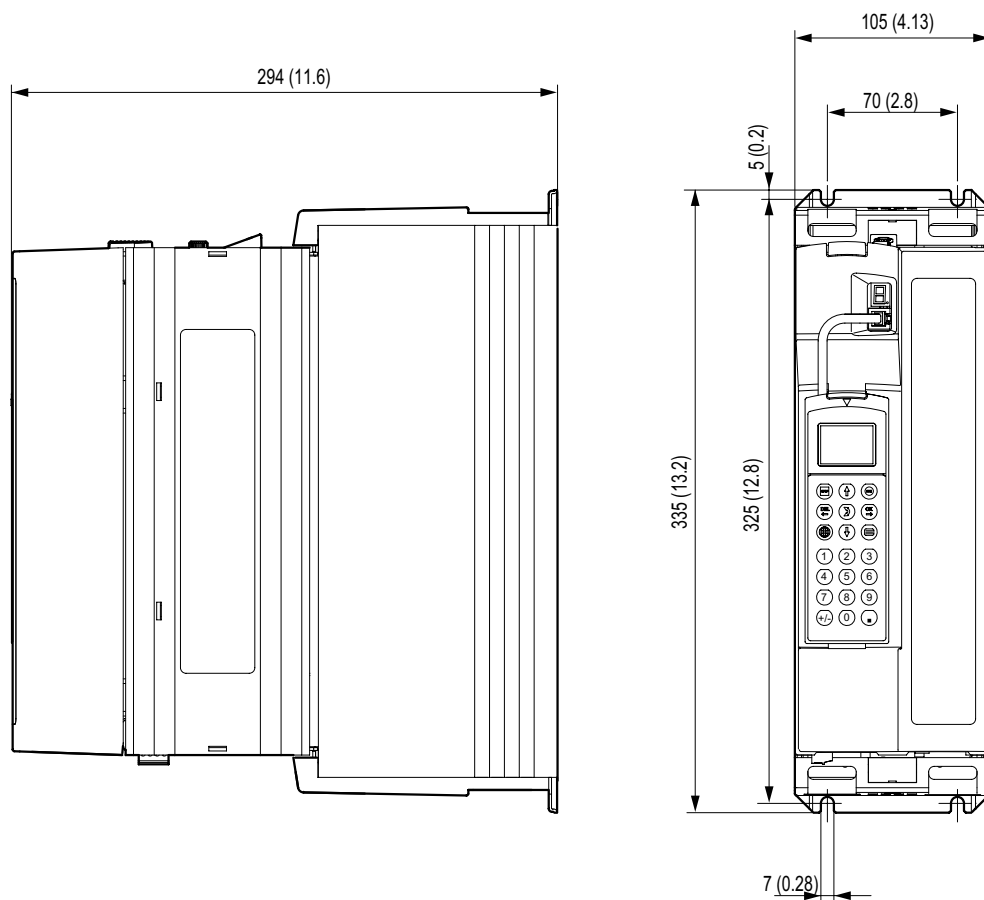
Dimensionais MDX61B, tamanho 2S, dimensões em mm (in)
